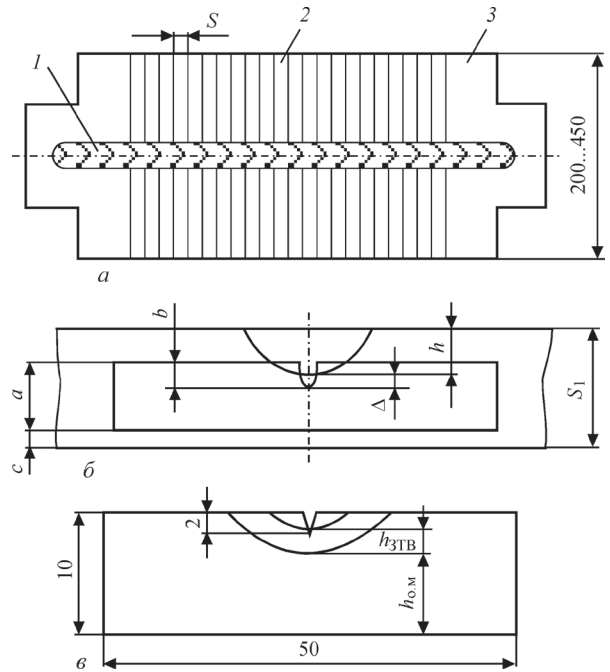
Валиковая проба с наплавкой (а), схема вырезки образцов для испытаний на ударный изгиб (б) и обозначение участков сварного соединения, которые входят в состав ударного образца (в): 1 — наплавленный валик; 2 — составные бруски; 3 — выводная планка; h — участок с наплавленным металлом; $h_{ЗТВ}$ — участок ЗТВ; $h_{о.м.}$ — участок основного металла
